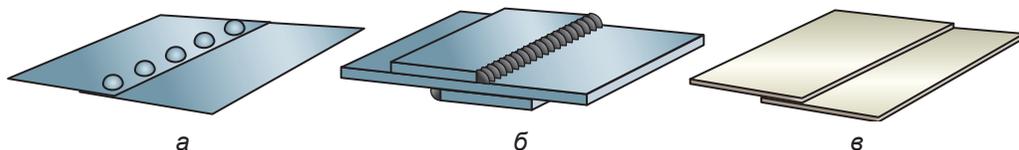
Виды неразъёмных соединений: а – заклёпочное; б – сварное; в – клеювое
